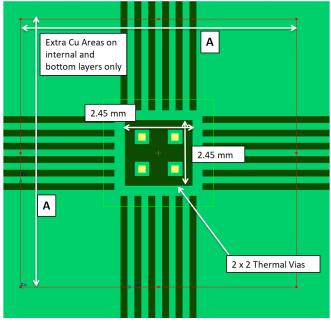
PCB - Top Layer (4/2-Layer PCB) for VQFN Package
